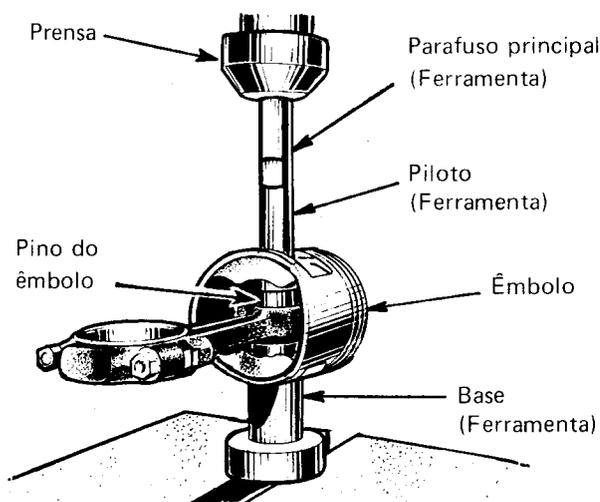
Remoção do pino do êmbolo com a ferramenta C-4158
